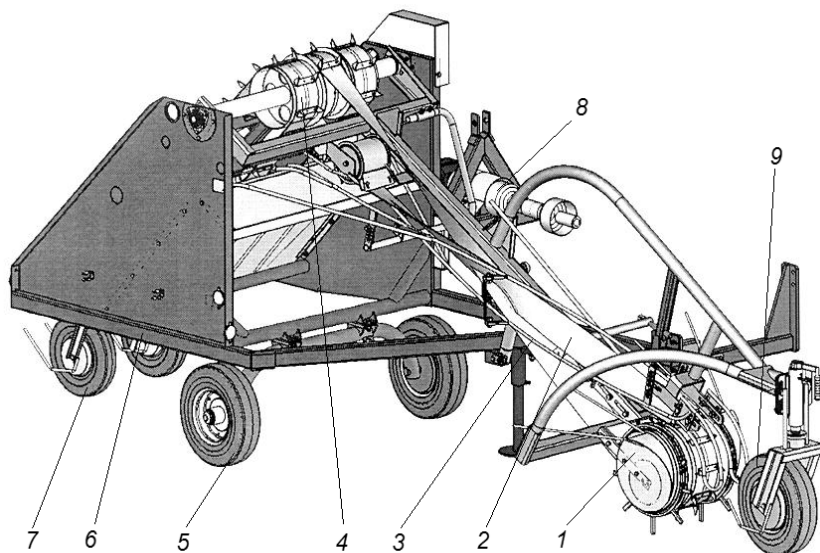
Полунавесной однопоточный оборачиватель ленточного типа:
